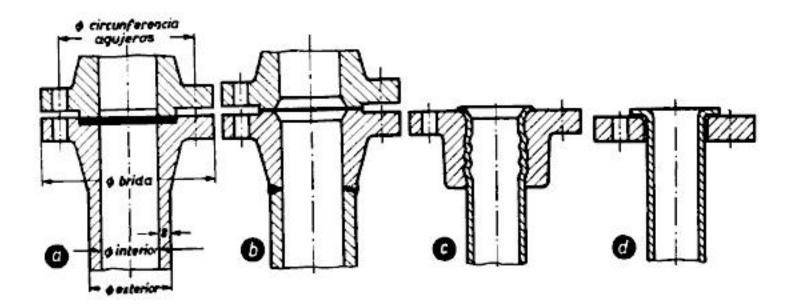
Platinas o bridas: a) Tubo de hierro fundido provisto de bridas; se emplea hasta presiones de 10 atm. b) Brida de hierro fundido soldada al tubo. c) Tubo de acero con brida adaptada al tubo por mandrilado. d) Tubo de acero rebordeado, con brida suelta. Observación: El número de agujeros para tornillos en las bridas debe ser divisible por 4. El cálculo del espesor de paredes en los tubos, según DIN 2412.
